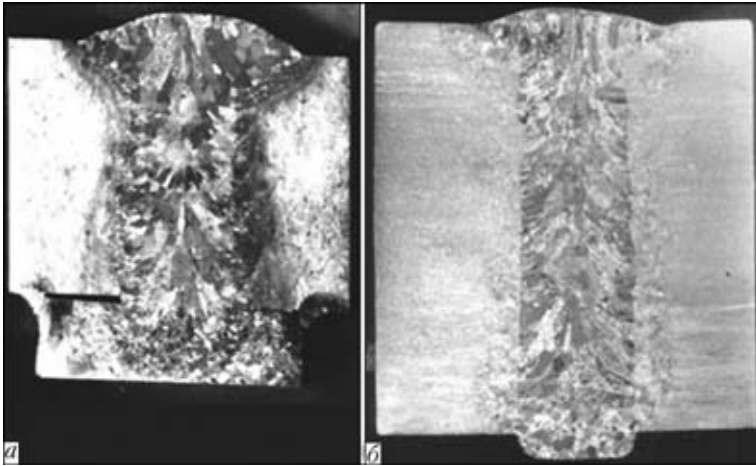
Макрошлифы сварных соединений, полученных сваркой ТИГ в узкий зазор с управляющим магнитным полем на остающейся (а) и формирующей (б) подкладке
